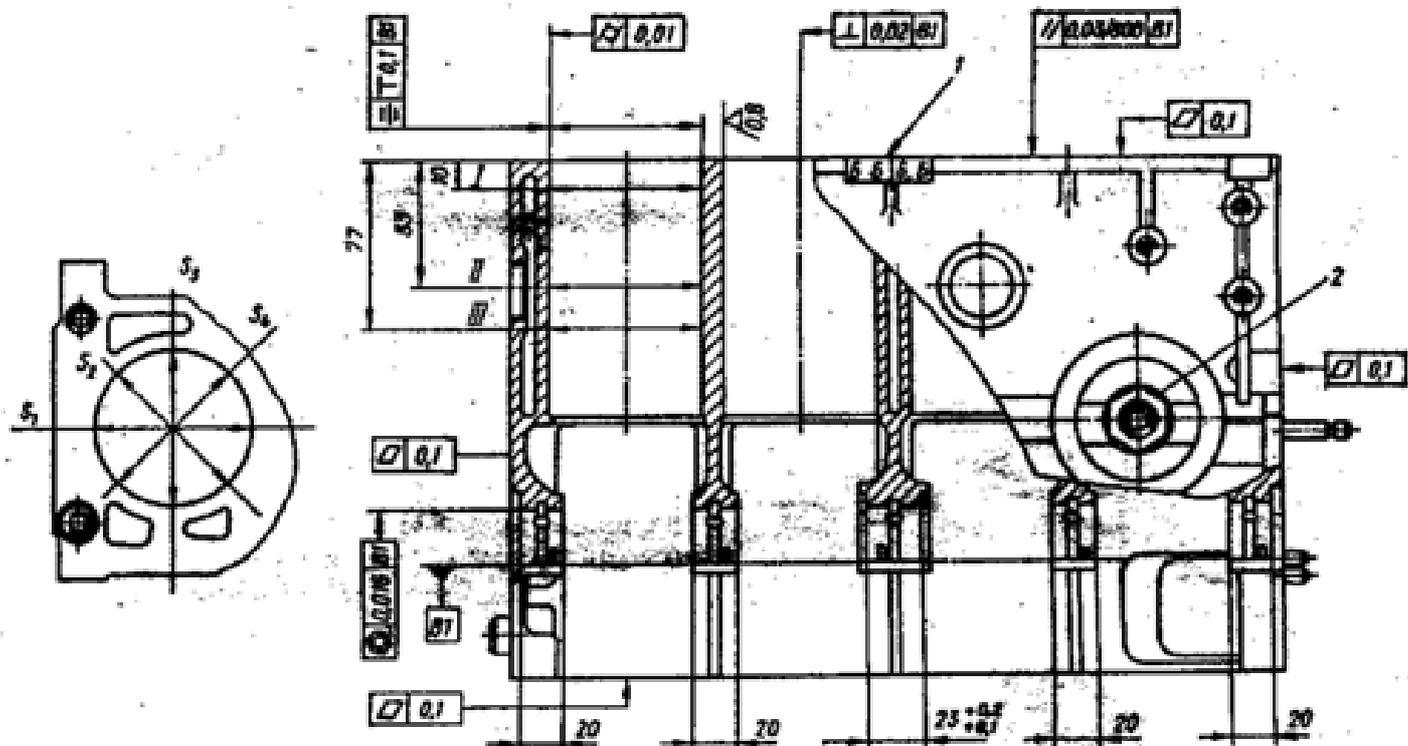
Блок цилиндров двигателя: 1 - место нанесения групп цилиндров; 2 - штуцер крепления масляного фильтра; S₁ - ось коленчатого вала
